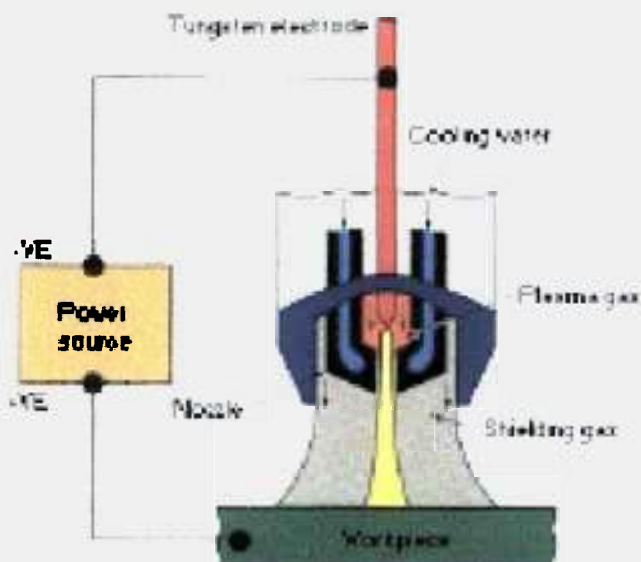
Tocha utilizada em soldagem plasma – corte transversal⁸⁵.
